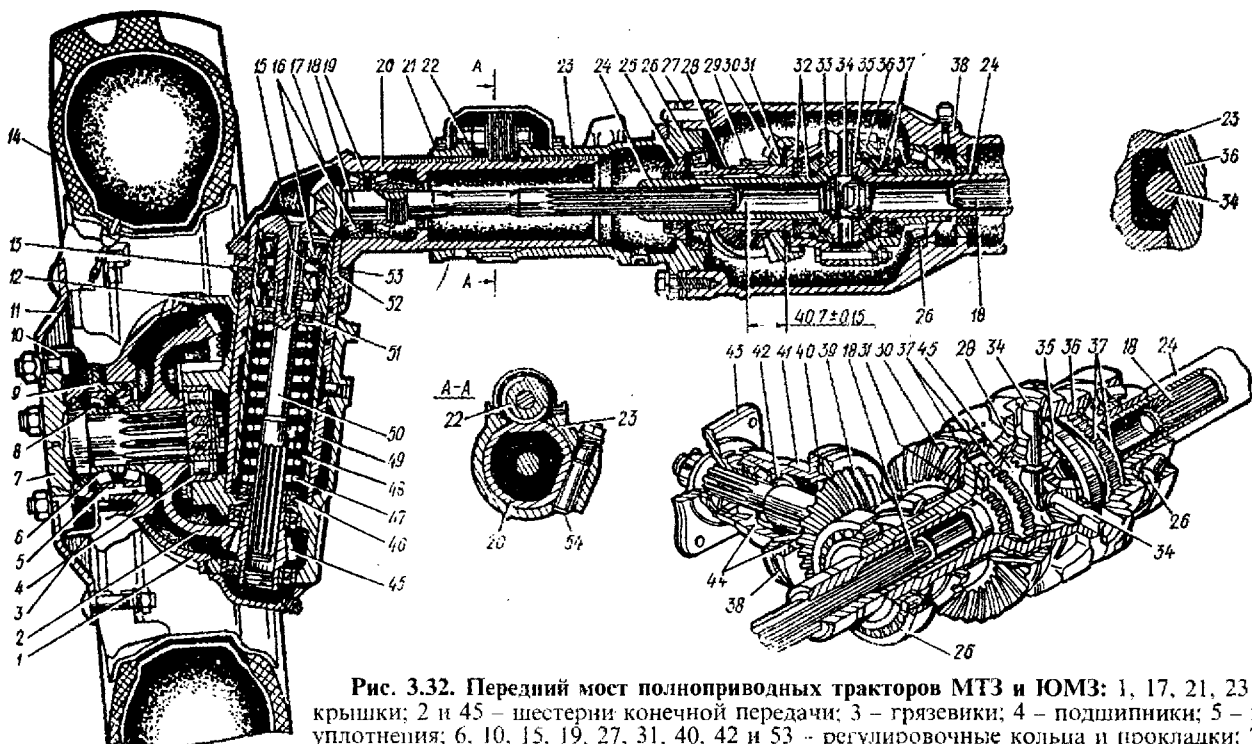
Передний мост полноприводных тракторов МТЗ и ЮМЗ: 1, 17, 21, 23 и 28 - крышки; 2 и 45 - шестерни конечной передачи; 3 - грязевики; 4 - подшипники; 5 - корпус уплотнения; 6, 10, 15, 19, 27, 31, 40, 42 и 53 - регулировочные кольца и прокладки; 7 - вал конечной передачи; 8, 16, 26 и 44 - конические подшипники; 9 и 41 - стаканы подшипников; 11 - диск колеса; 12 - корпус конечной передачи; 13 - стакан; 14 - ведущее колесо; 18 - полуоси; 20 - выдвижной корпус; 22 - червяк; 24 - полуосевые шестерни; 25 - корпус дифференциала; 29 - гайка; 30 и 39 - шестерни главной передачи; 32 и 37 - фрикционные диски дифференциала; 33 - нажимная чаша; 34 - оси сателлитов; 35 - сателлит; 36 - корпус; 38 - корпус моста; 43 - фланец; 46 - шариковый упорный подшипник; 47 - пружина; 48 - вихоревая труба; 49 - гильза; 50 - вертикальный вал; 51 - упорная шайба в сборе с уплотнителем; 52 - упорный фланец; 54 - клиновидный болт
